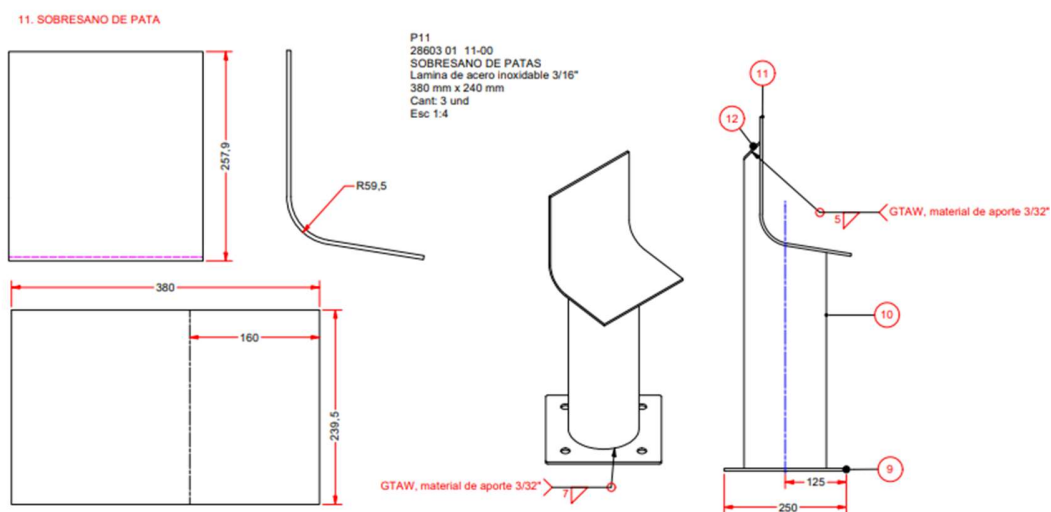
Desarrollo y soldadura de sobresano para pata de tanque.
